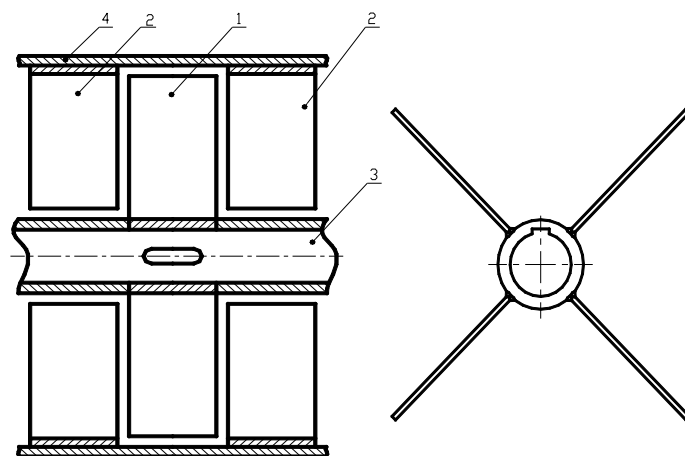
Конструктивна схема проточної частини ТГА
